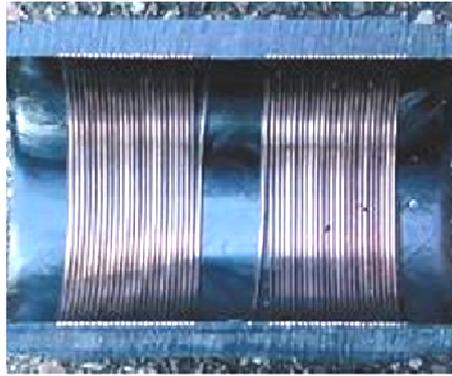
Общий вид разреза электромуфты для терморезисторной сварки
